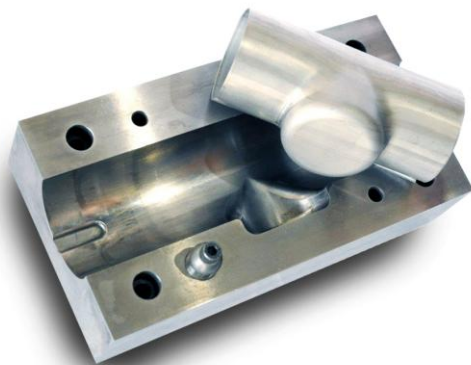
IHU-Werkzeug mit umgeformtem Bauteil (T-Stück).
